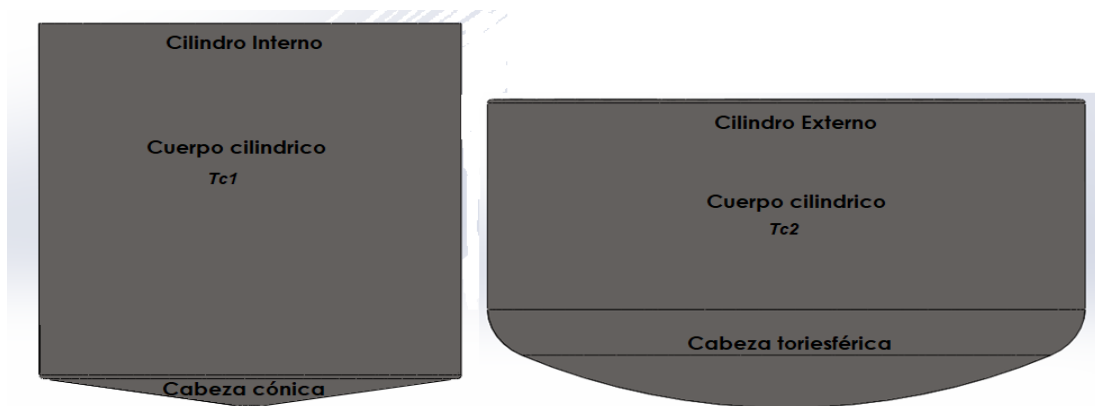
Vista frontal del tanque interno y externo que componen la marmita
